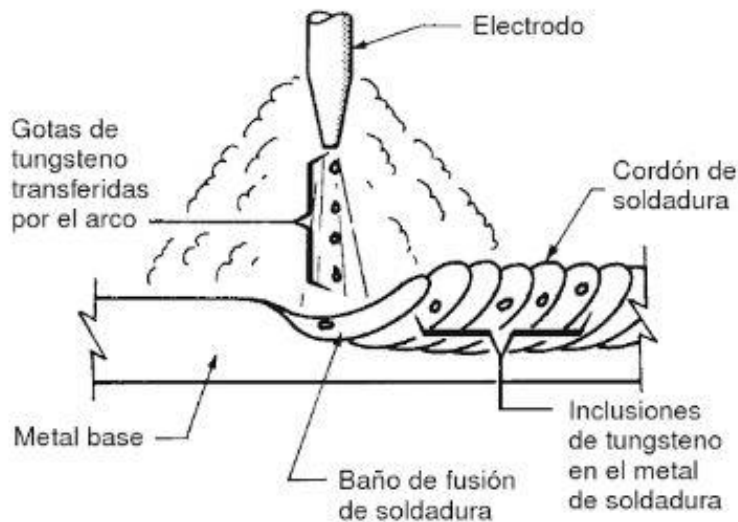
Proceso de soldadura metálica GTAW, [17].
